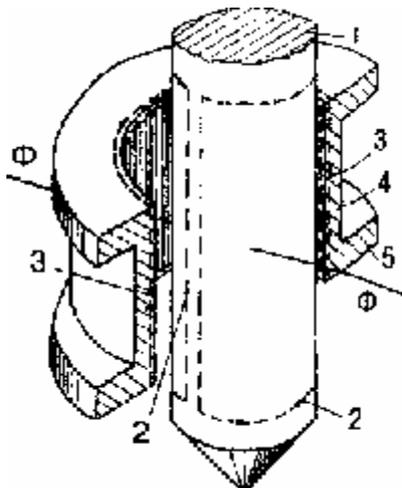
Вихретоковый преобразователь в контролируемом отверстии: 1 - датчик; 2,2а - возбуждающая и измерительная обмотки; 3 - вихревые токи; 4 - трубка меди; 5 — контактная площадка; Φ - радиальный магнитный поток.
